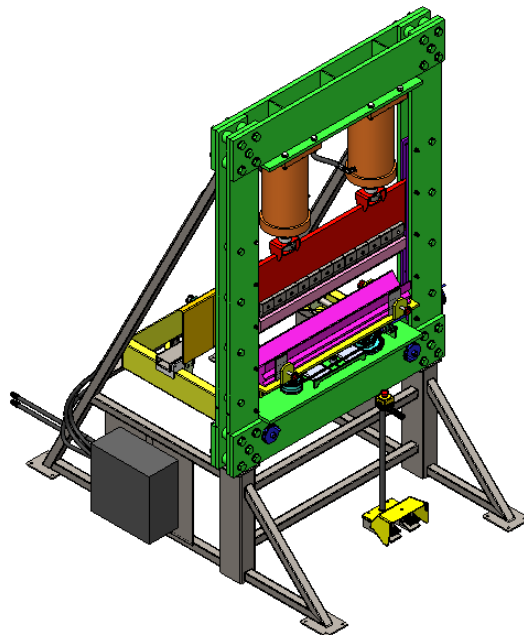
Modelo 3D final de la parte mecánica. Vista isométrica 2.
